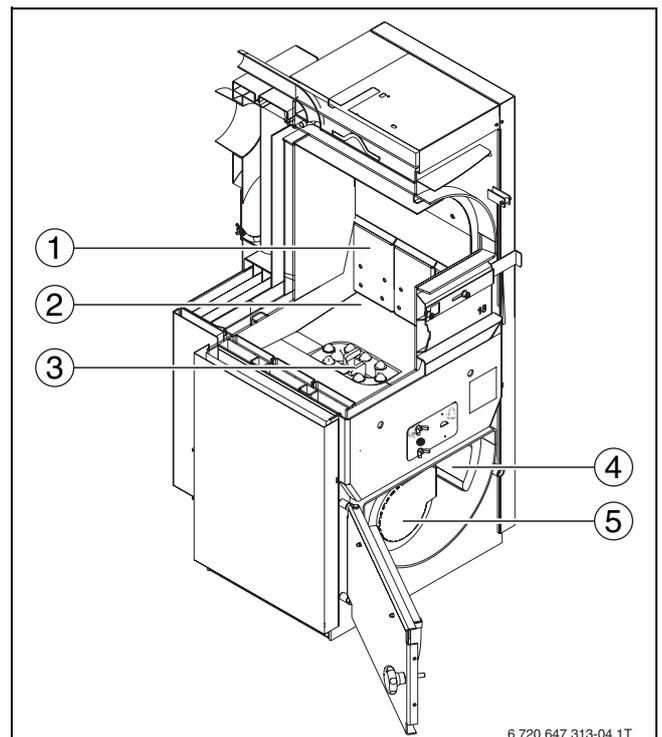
Pavimento del vano di carico con deflettore in ghisa
